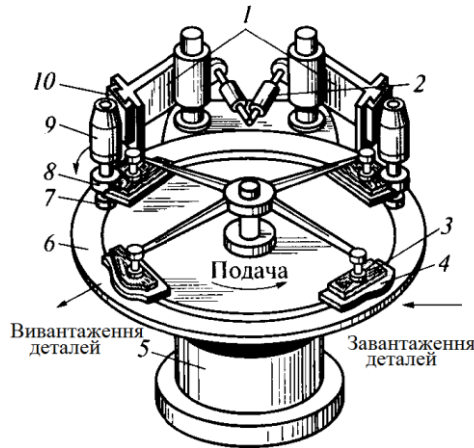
Двошпиндельний фрезерний карусельний верстат: 1 – поворотні кронштейни; 2 – пневмоциліндр; 3 – пневматичний притиск; 4 – шаблон; 5 – станина; 6 – карусельний стіл; 7 – копіювальне кільце; 8 – фреза; 9 – електродвигун; 10 – супорт
